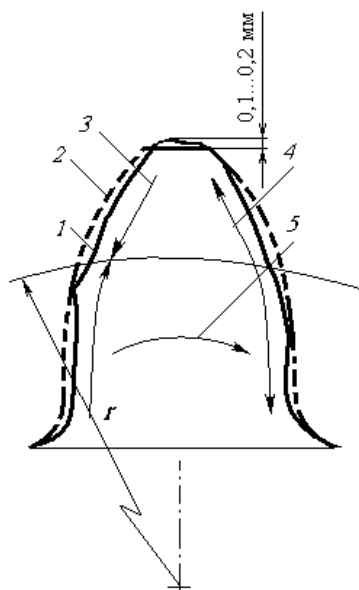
Характер течения металла зуба вследствие пластического деформирования при накатывании: 1 – профиль накатанного зуба; 2 – профиль фрезерованного зуба; 3, 4 – направления течения металла на приводной и не приводной стороне зуба; 5 – направление вращения заготовки; r – радиус начальной окружности.
